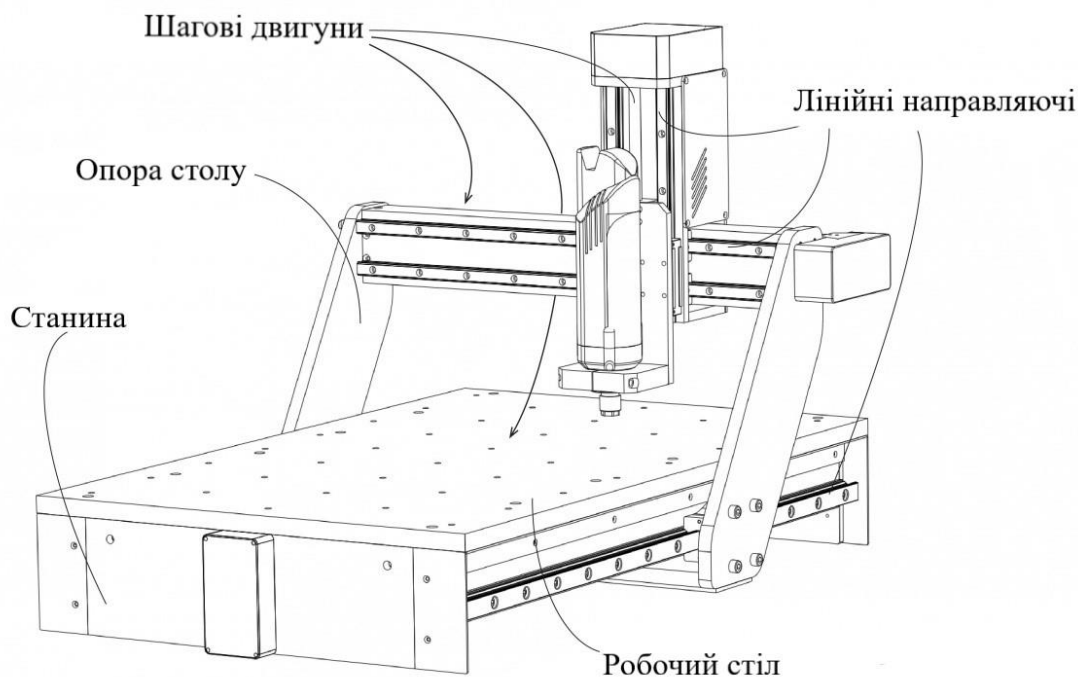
CAD проект фрезерного верстату з ЧПК.
